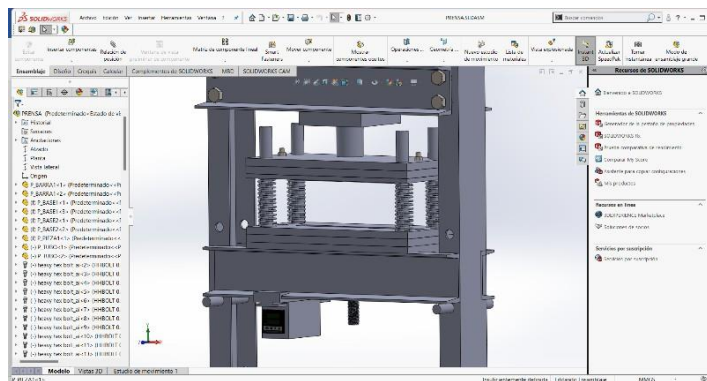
Presa hidráulica con el mecanismo instalado Vista a Detalle.
